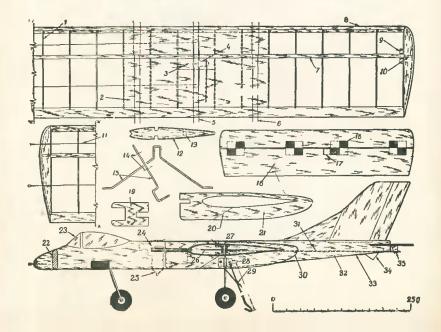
Компоновочная схема двухмоторной кордовой модели: 1— проволока 1,5 мм; 2— поверхность, покрытая красной краской; 3— поверхность, покрытая черной краской или изготавливаемая из плексигласа 1 мм; 4— фюзеляж плоского сечения из хорошо просушенной сосновой планки 10 мм; 5— колено передней ноги шасси; 6— обойма крепления передней ноги шасси из алюминия; 7— передняя нога шасси из стальной проволоки 2,5 мм; 8— колесо 40 мм; 9— красная полоса на фюзеляже;
